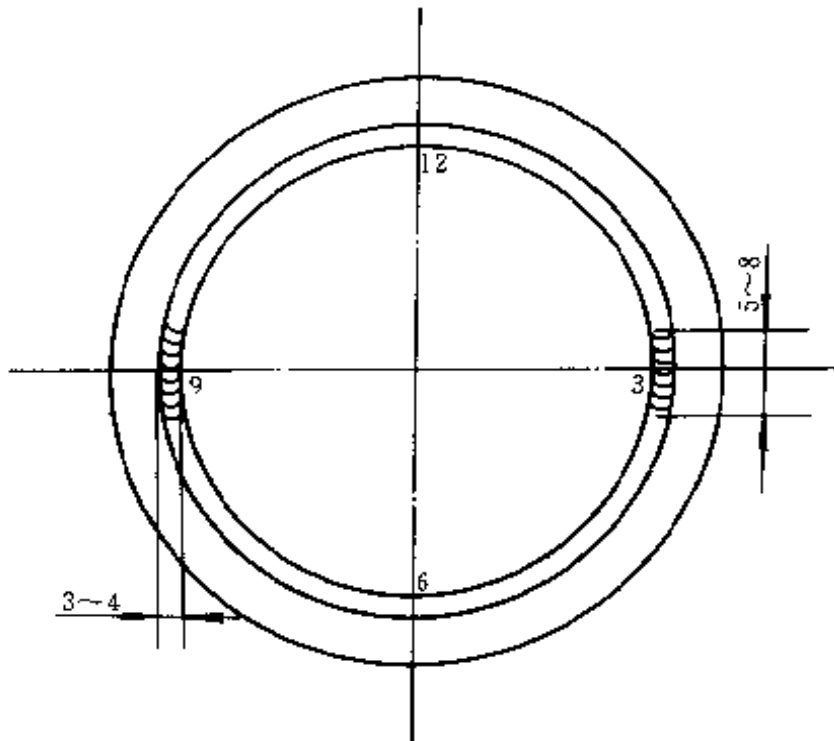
29 管对接垂直固定障碍焊定位焊缝的位置
